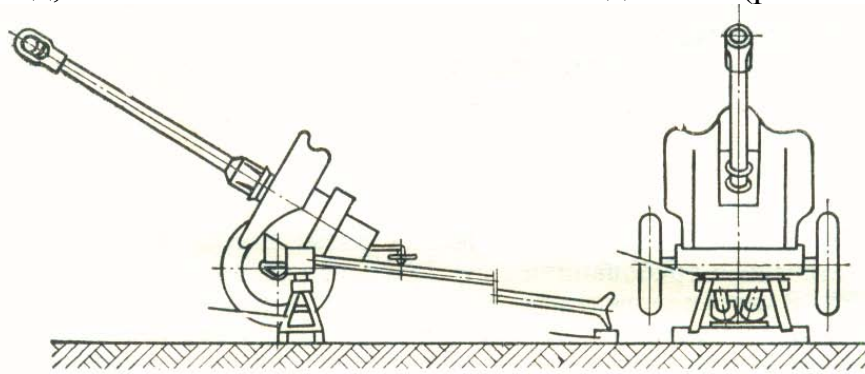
Установка причіпної артилерійської гармати на козелки
